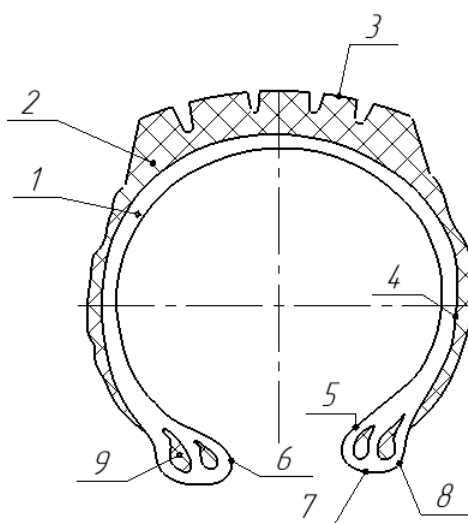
Конструктивные элементы шины: 1 – каркас; 2 – брекер; 3 – протектор; 4 – боковина; 5 – борт шины; 6 – носок борта; 7 – основание борта; 8 – пятка борта; 9 – бортовые кольца [52]
